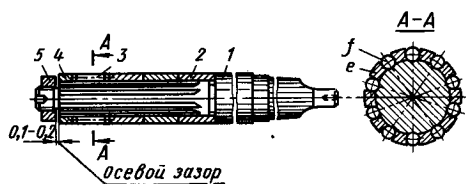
Раскатка ударного действия для отверстий диаметром до 30 мм: 1 — корпус оправки; 2 — промежуточное кольцо; 3 — ролики; 4 — сепаратор; 5 — гайка
